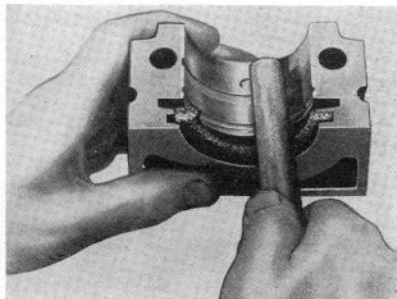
Chapeau de palier arrière du vilebrequin.
